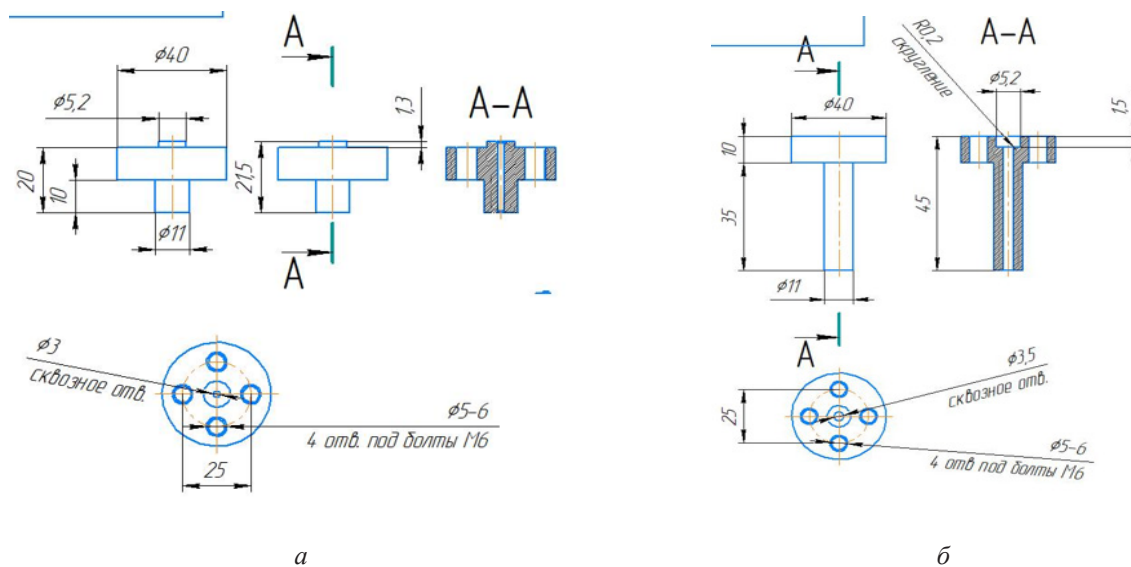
Чертеж разработанной конструкции для проведения испытаний круглых компактных образцов конструкции
